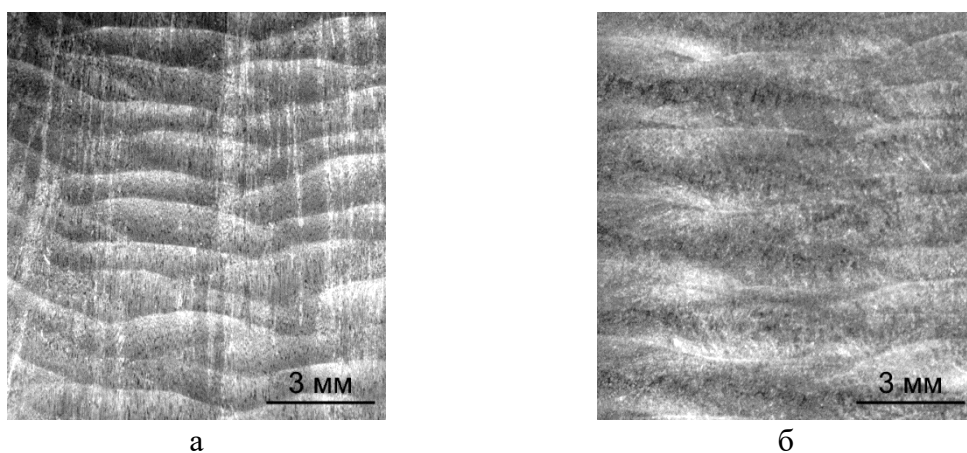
Макроструктура наплавленного металла: а – при наплавке без послойной проковки, б – при наплавке с послойной проковкой
